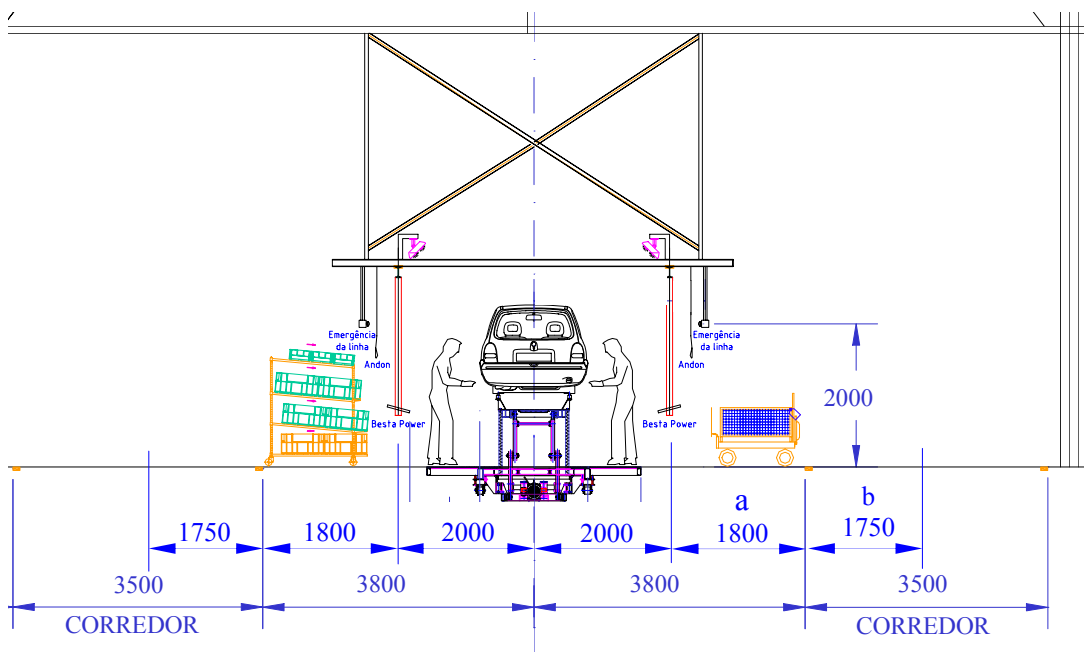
Corte típico da linha de montagem da Planta SJC (cotas em milímetros)
